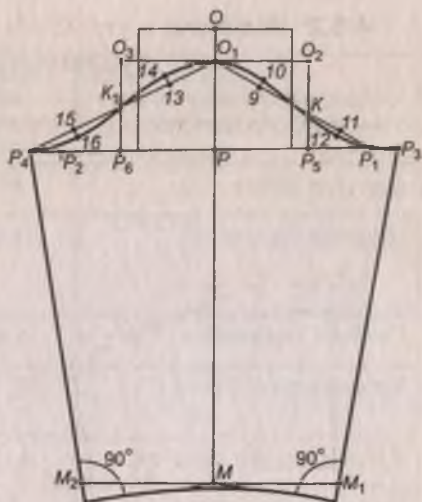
Чертеж конструкции рукава рубашечного покроя
